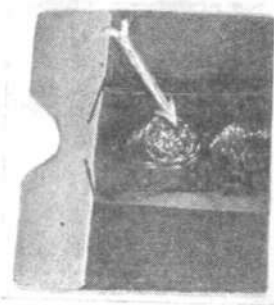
Прожог (подплавление подкладного кольца) при ручной дуговой сварке.
